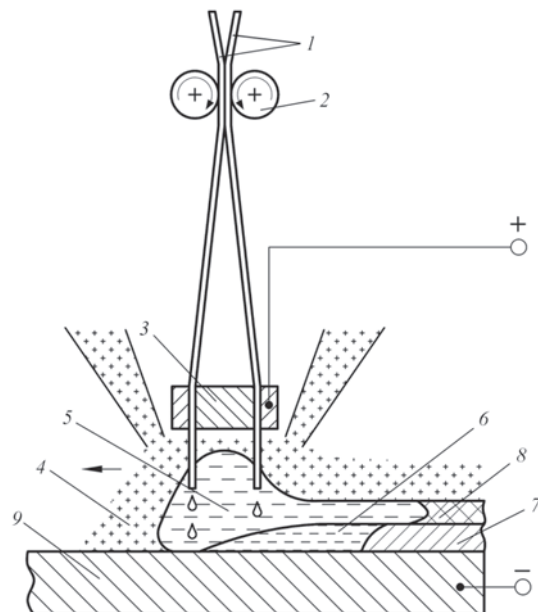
Схема электрошлаковой наплавки двумя лентами [4]: 1 — электродные ленты; 2 — подающие ролики; 3 — медная вставка-токоподвод; 4 — флюс; 5 — шлаковая ванна; 6 — металлическая ванна; 7 — наплавленный металл; 8 — шлаковая корка; 9 — наплавляемая заготовка
